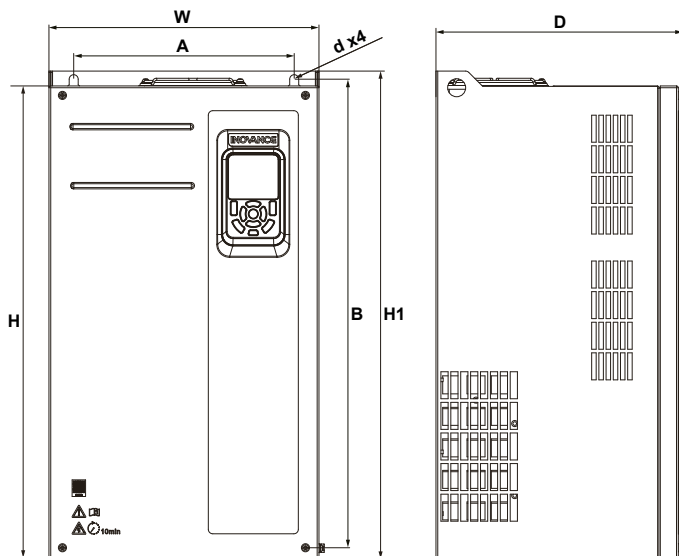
Внешний вид типоразмеров T7 - T9
